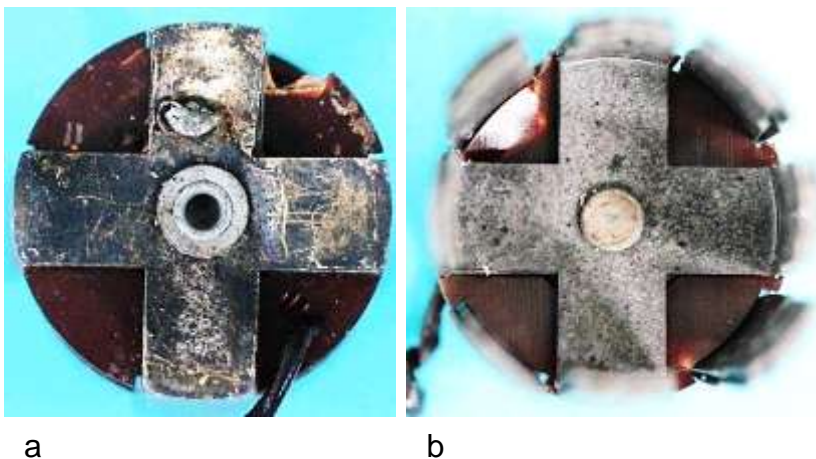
Kreuzbleche a) Unterseite mit Messingblech, b) Blick durch den zylindrischen Polradraum auf das obere Joch
